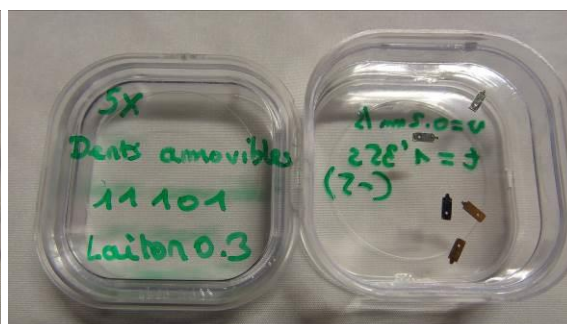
Vue macroscopique, v=0.8 mm/s.
